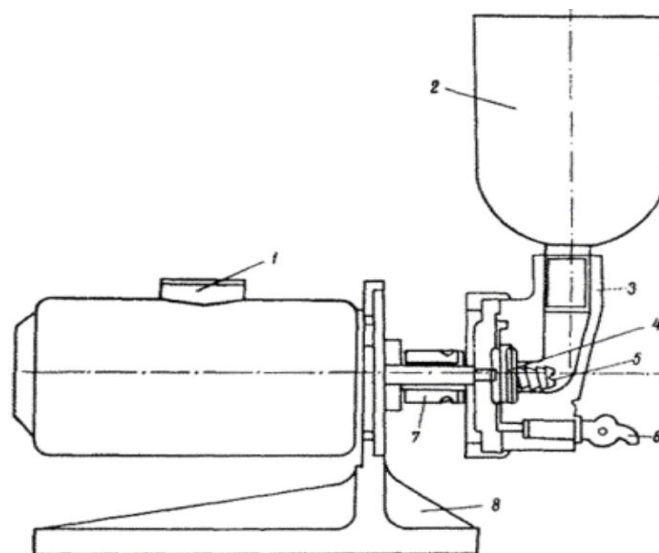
Схема диспергатора СПЕМ-2/1,0-ВК-Р32 [190]: 1 – електромотор УЛ-62 №-0,270 кВт, 8000 об/хв; 2 – воронка; 3 – корпус; 4 – турбінка (змішувач); 5 – шнек; 6 – кран; 7 – гайка; 8 – стійка
